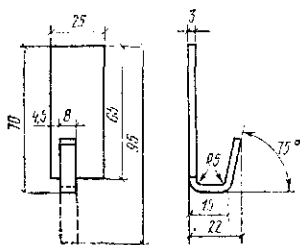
Крючки типа 23кс (масса 0,039 кг) для крепления высоко расположенных смывных бачков на кирпичных или бетонных стенах дюбель-гвоздями
